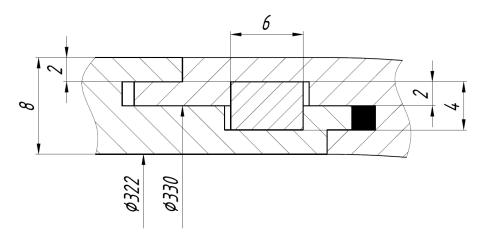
Элемент крепления корпуса и соплового блока.
